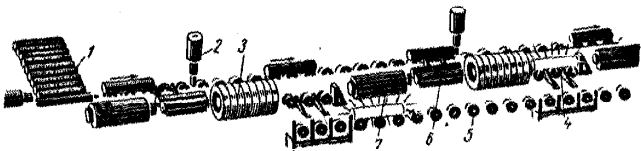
Схема нагревателя с двумя периодическими индукторами: 1 — магазин для заготовок; 2 — убирающийся упор, останавливающий заготовку; 3 — рольганг для подачи заготовок на площадку 6; 4 — механизмы для выдачи нагретых заготовок; 5 — рольганг для транспортировки нагретых заготовок; 6 — площадка перед индуктором на несколько заготовок; 7 — толкатель для подачи заготовки в индуктор.
